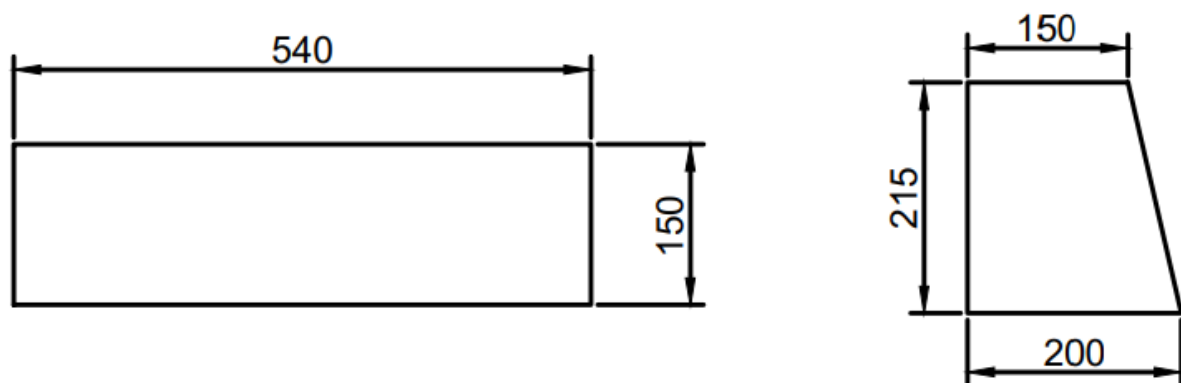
Dimensiones del estabilizador horizontal (izquierda) y vertical (derecha)
